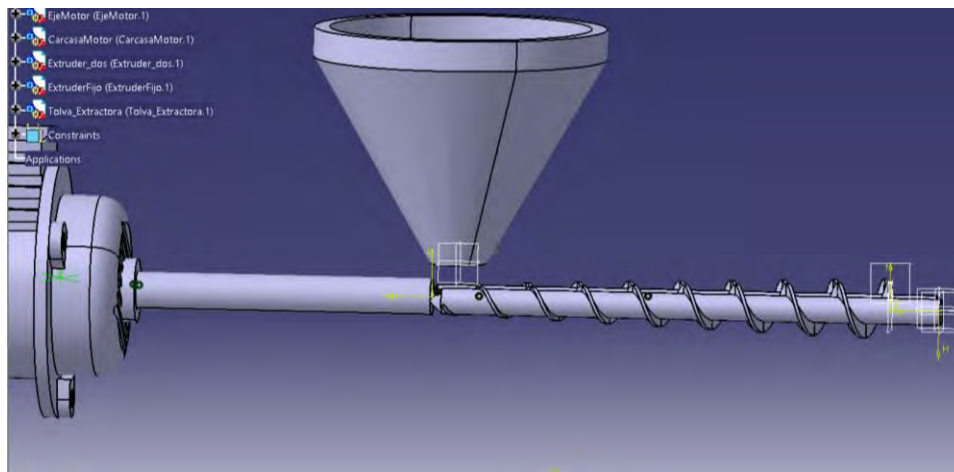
Ensamble mecánico del mecanismo de extracción de aceite (realizado en Catia V5)
